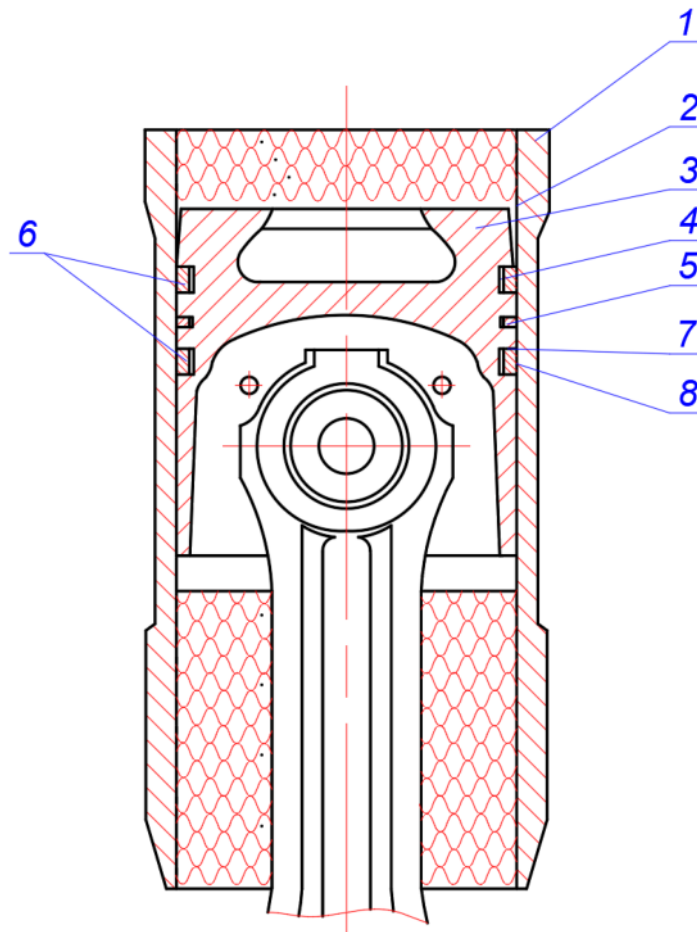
Циліндро-поршневий механізм двигуна внутрішнього згорання
